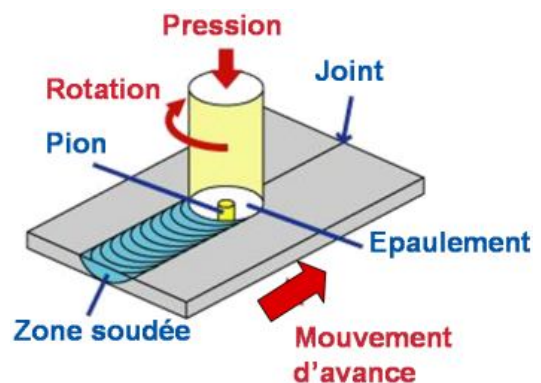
Présentation du soudage par friction malaxage [5]
